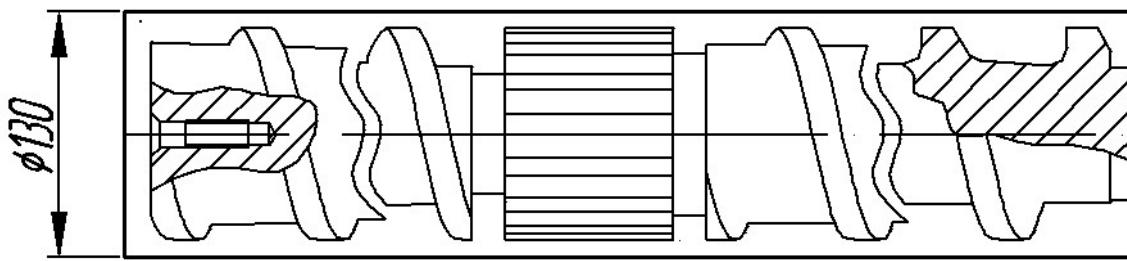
Ескіз заготовки із круглого прокату
